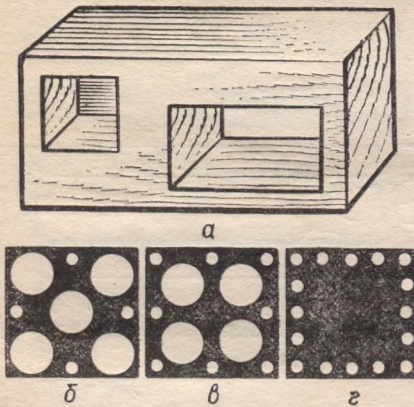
Изготовление глухого (сквозного) отверстия квадратной формы:
